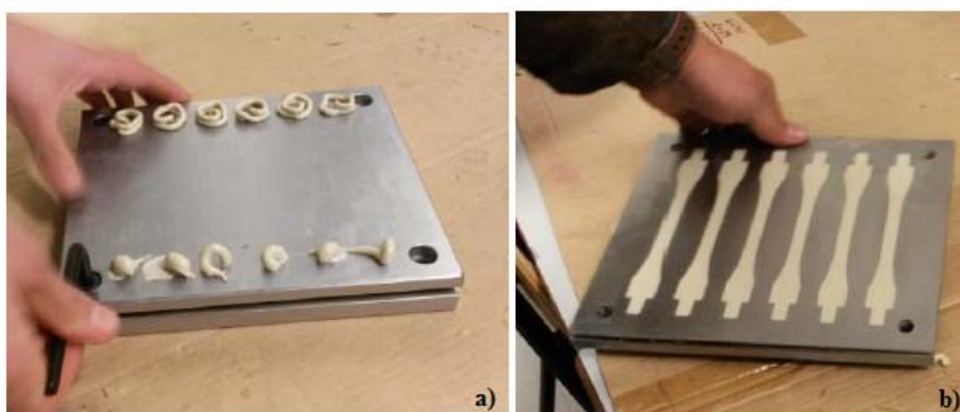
Abertura do molde: a) desaperto do molde e b) aspeto dos provetes ainda no molde, antes da desmoldação
